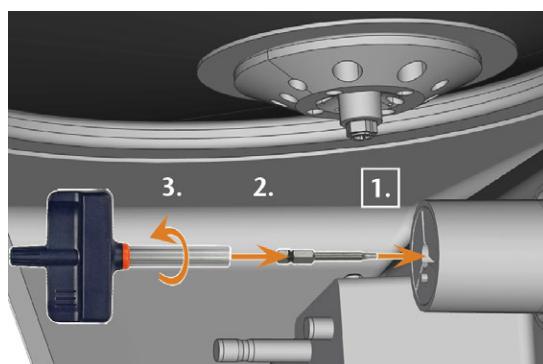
ALLENARE LA VITE DELLA PINZA DI SERRAGGIO DEL PORTAPEZZI
